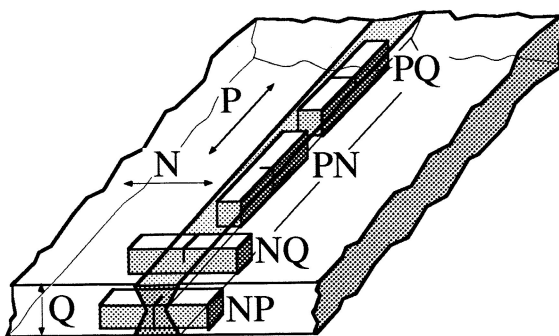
Definierte Probenlage in der Schweißnaht /102/
